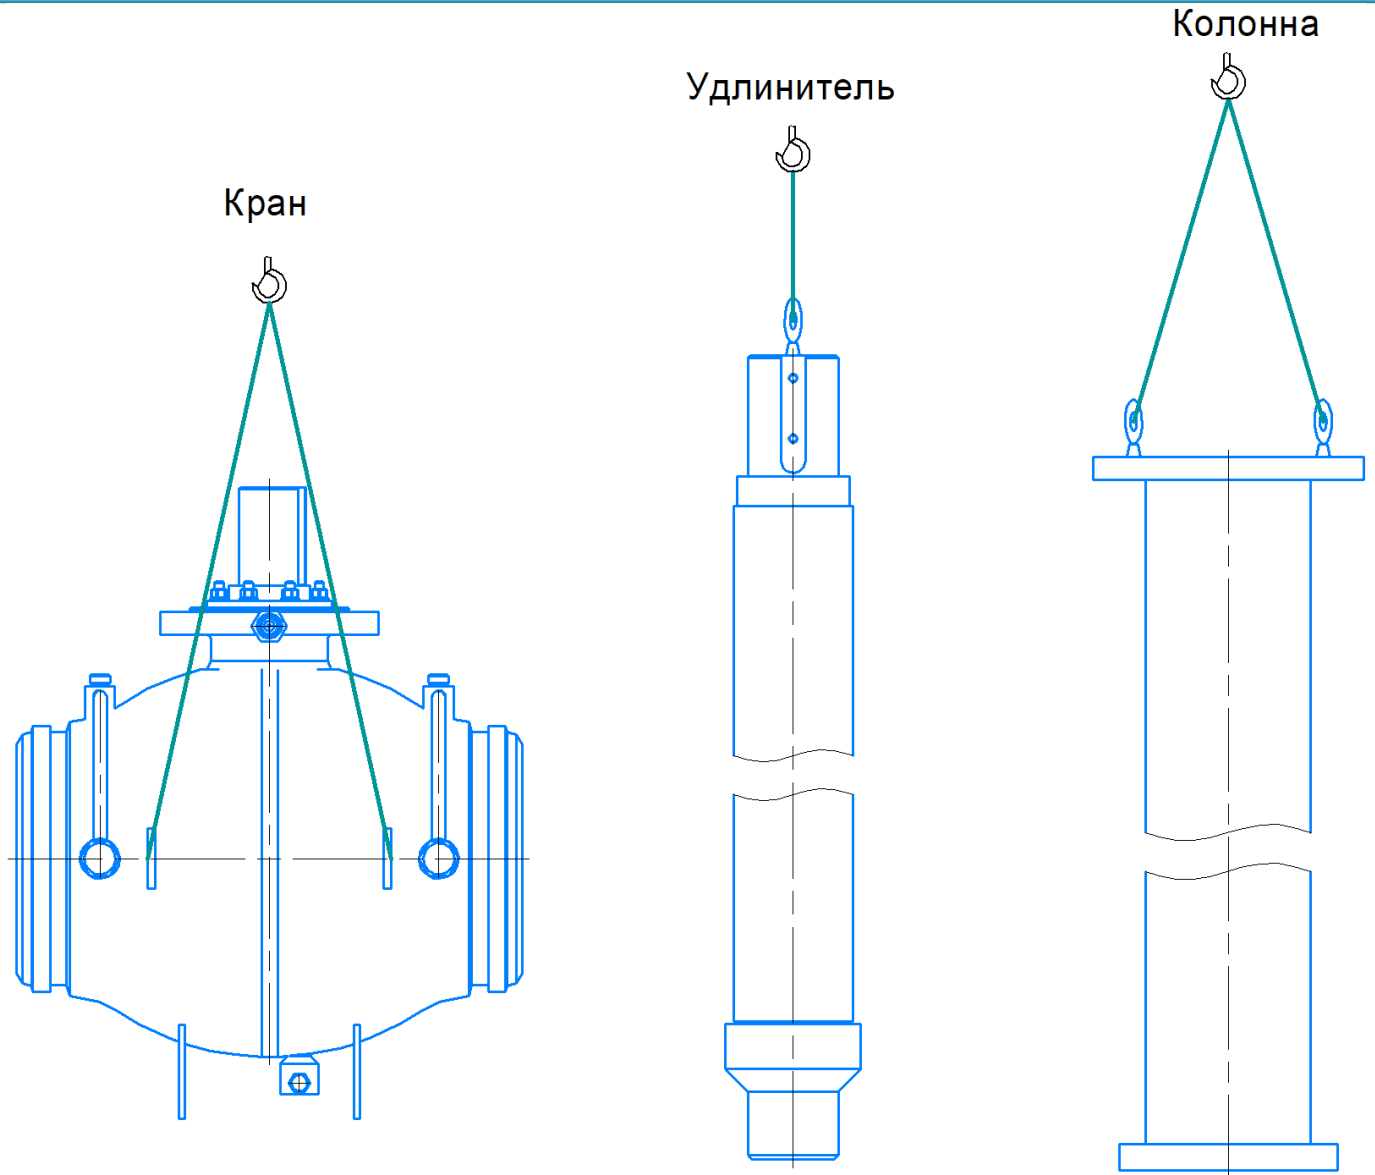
Схема строповки узлов подземного крана при монтаже (рекомендуемая)
